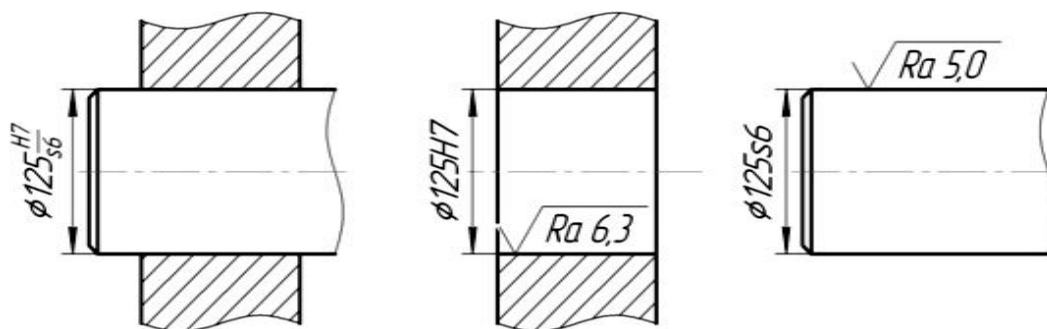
Обозначение посадки и полей допусков деталей на чертежах
